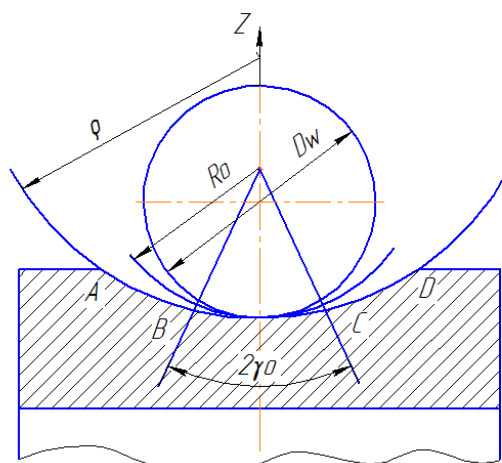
Сложный профиль желоба кольца подшипника [5]
